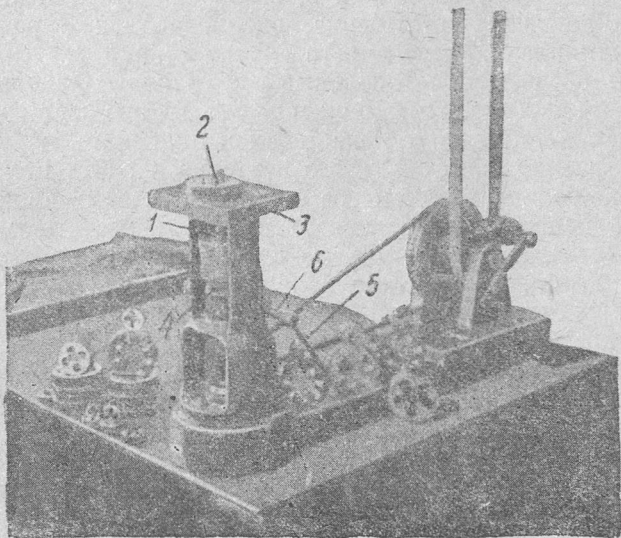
Специальный станок для заточки лерок фирмы Ган и Кольб.
